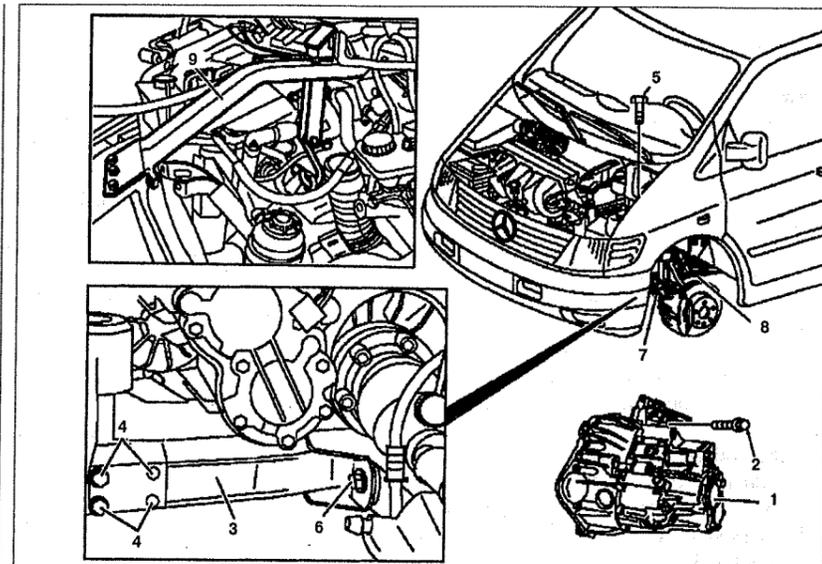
Снятие и установка коробки передач (автомобили с двигателем 611.980):
